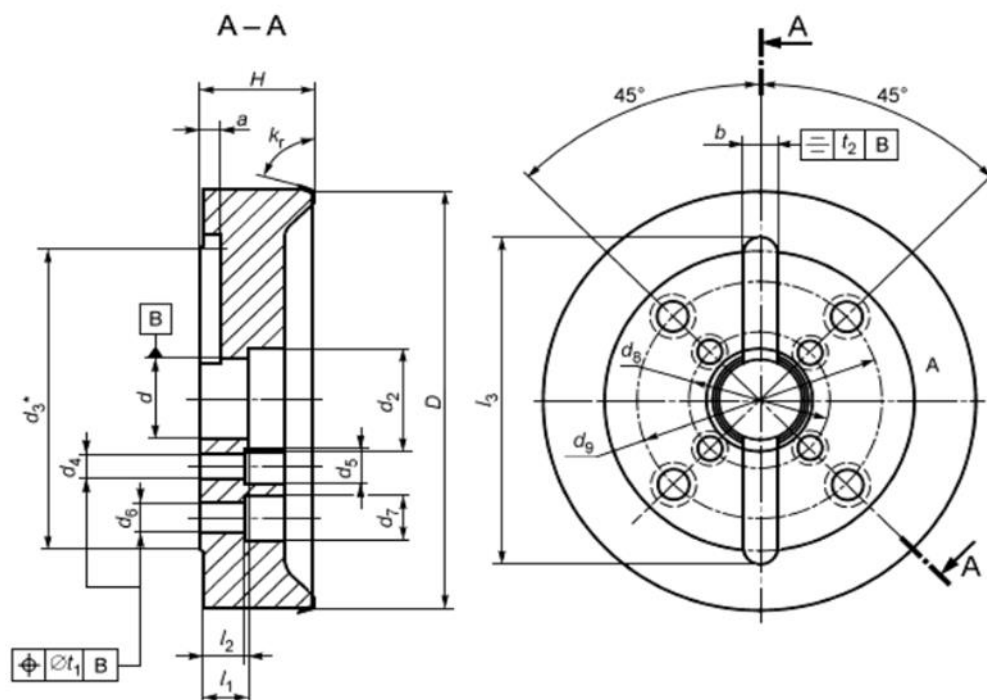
Корпус фрезы за ГОСТ 26595-2014[20]
